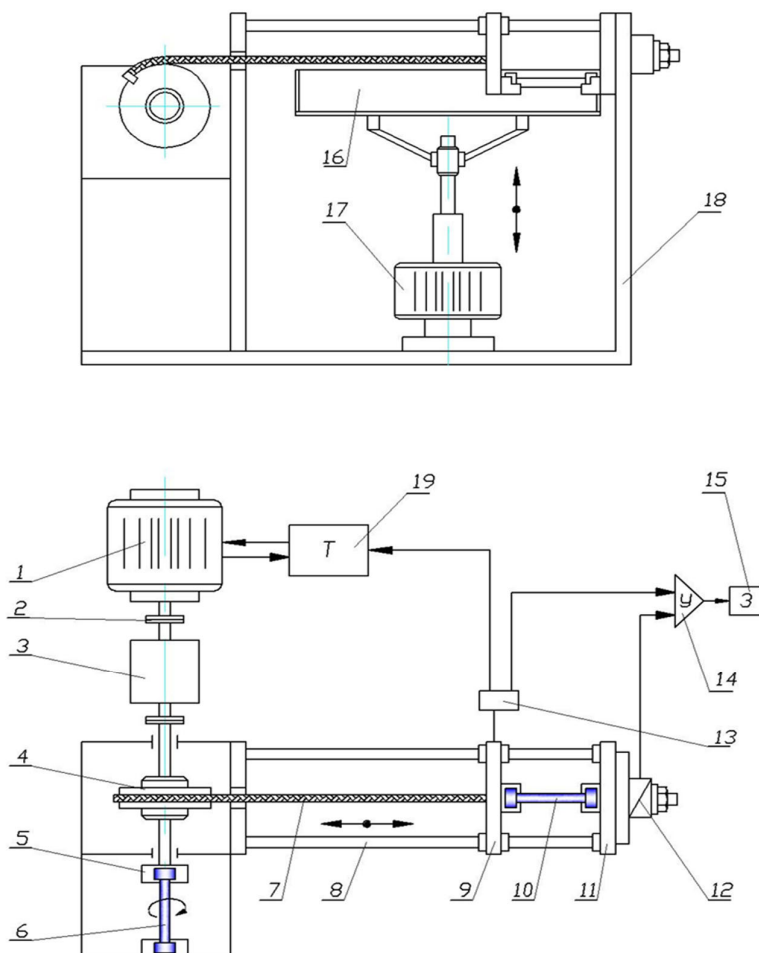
Схема за получаване на кръгли заготовки чрез право пресоване
